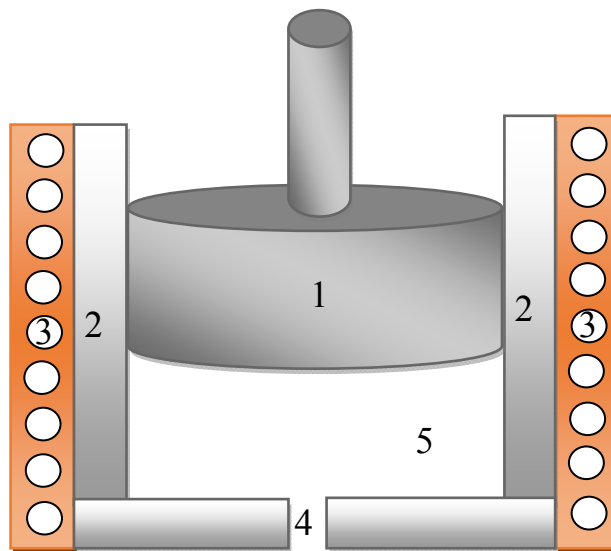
Схематичне зображення поршневого екструдера: 1 – поршень, який обертається; 2 – циліндрична основа; 3 – нагрівач; 4 – отвір для отримання ниткоподібного матеріалу; 5 – порошкоподібний композит
